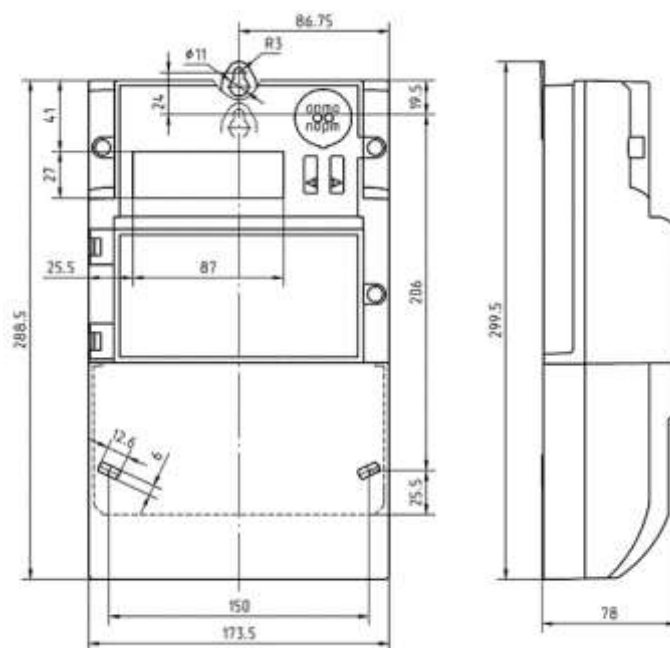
Внешний вид и габаритные размеры счетчика марки Меркурий 234 ARTM
